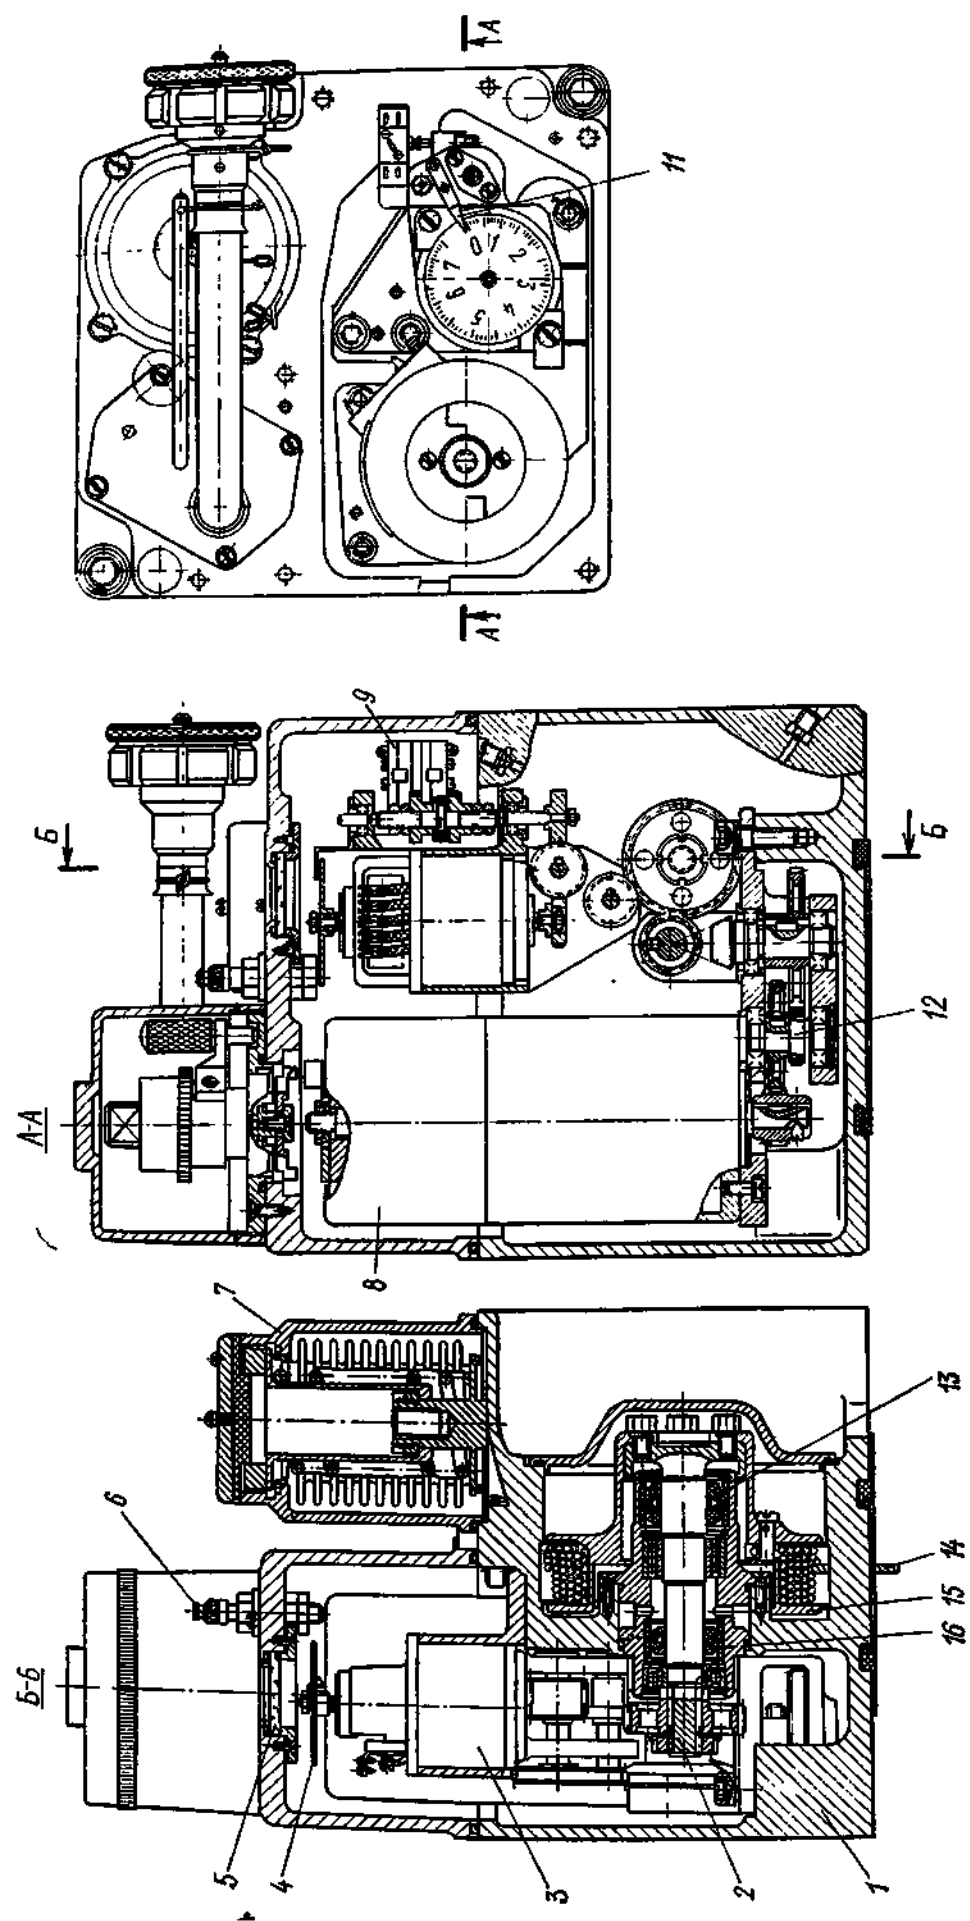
Конструкция привода РР — АЗ реактора РБМК
